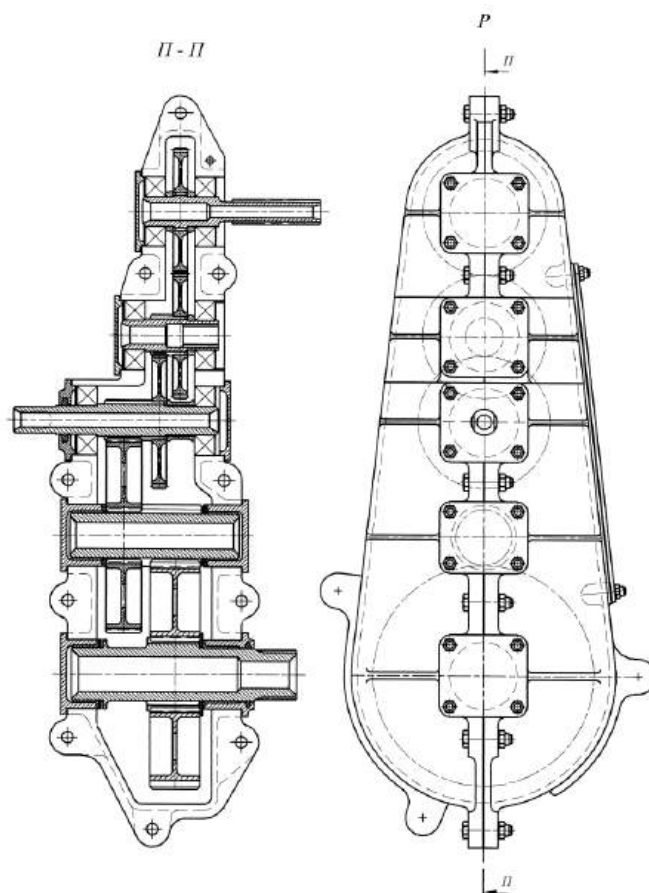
Загальний вигляд редуктору приводу здвигу
